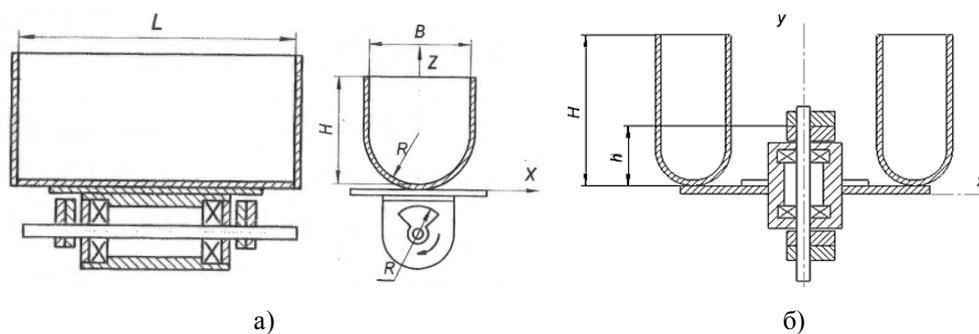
Схема компонування інерційного вібратора і робочої камери: а – з U-подібною робочою камерою; б – з тороїдальною робочою камерою
